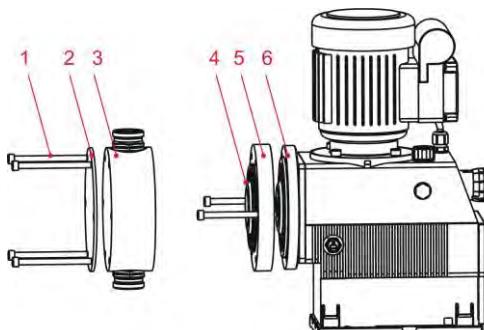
Austausch des Pumpenkopfes und der Membrane
